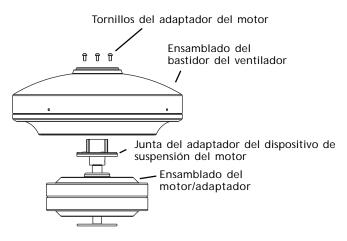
Como ensamblar y acoplar el bastidor al adaptador del dispositivo de suspensión del motor.
